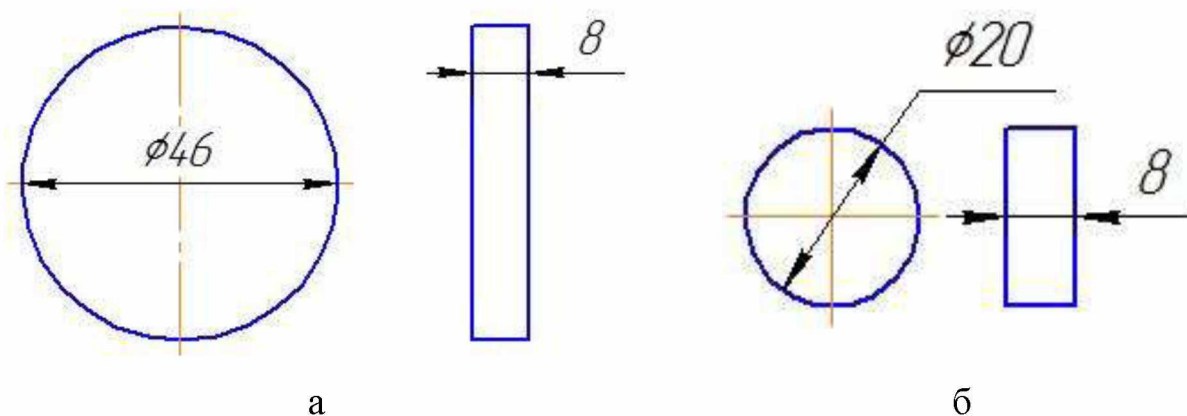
Зразки для вимірювання шорсткості поверхні
